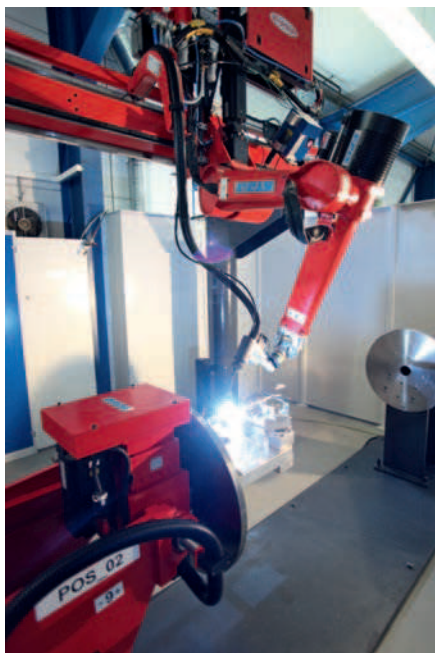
• Spritzerfreies Schweißen, das nur ein Minimum an Wärme ins Bauteil einbringt.
